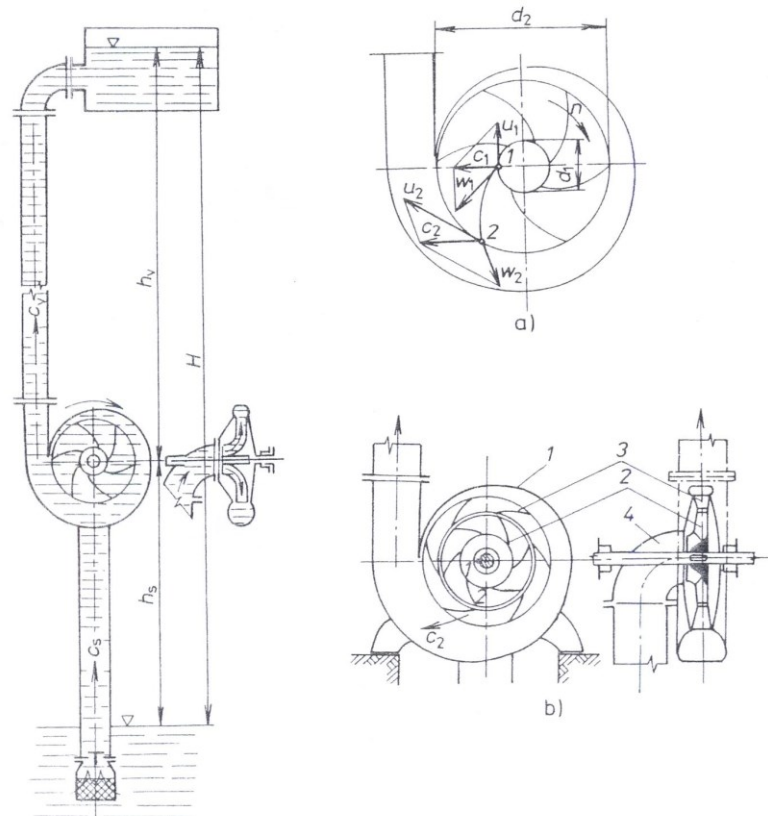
Odstředivé jednostupňové radiální čerpadlo a rotor čerpadla [7.2]
